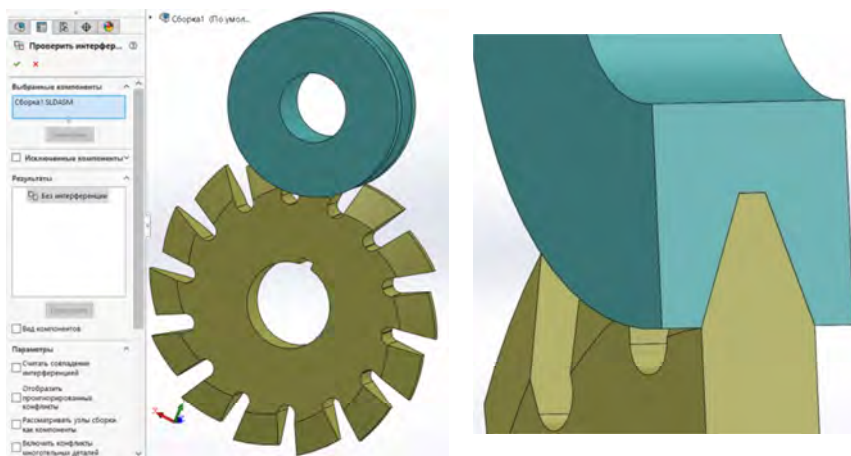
Сборка дисковой фрезы и шлифовального круга
